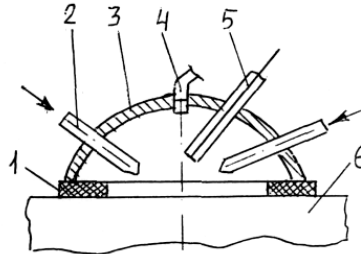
Схема електрогідравлічного очищення великих заготовок: 1 – гумова прокладка; 2 – патрубок для робочої рідини; 3 – ковпак кулястий; 4 – механічний маніпулятор; 5 – електроди; 6 – заготовка
